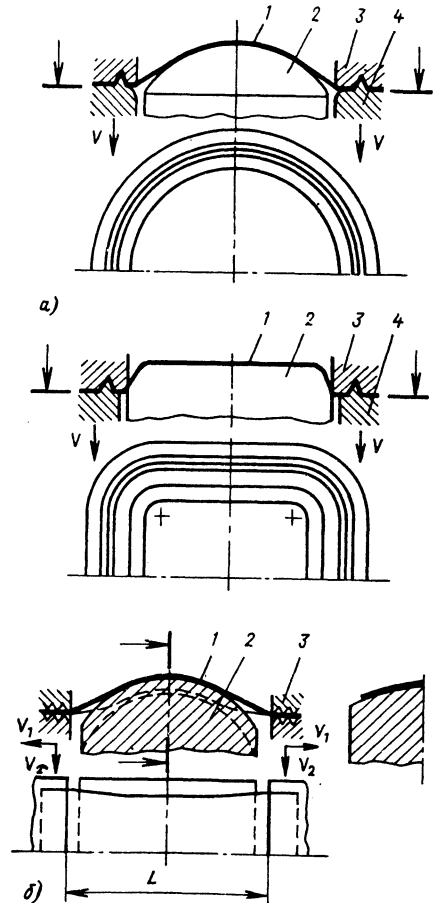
Формоизменение листовой заготовки растяжением и обтягиванием по пуансону:
